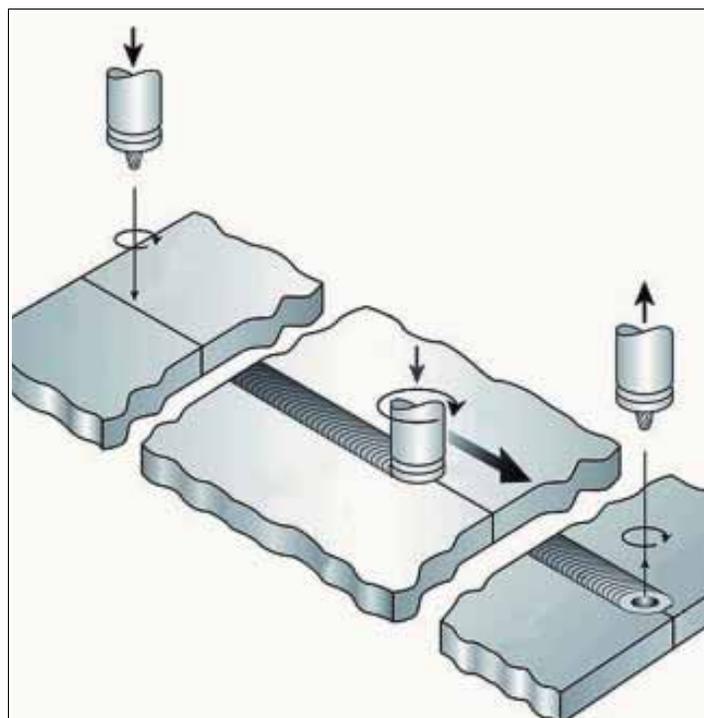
Schéma du procédé friction stir welding (source: ISO/DIS 25239-1)
